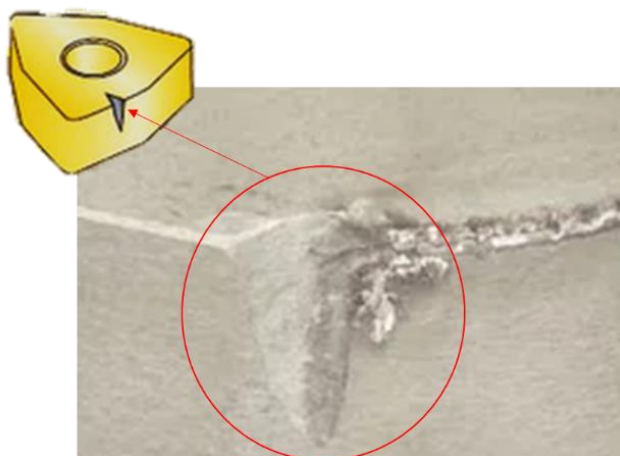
Desgaste de Flanco e Cratera na Usinagem de um Aço Rolamento AISI 52100
